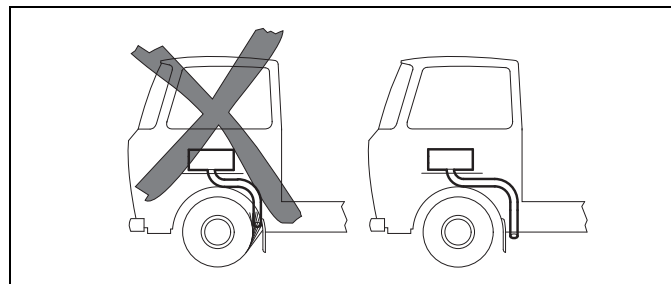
Éviter toute obstruction provoquée par un encrassement
